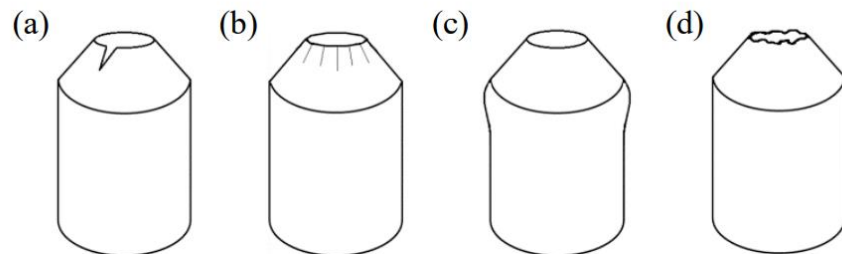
Дефекти, що виникають при обтисканні трубчастої заготовки обкочуванням: а) розриви; б) полігональні гофри; с) втрата стійкості; d) гофри [28]
